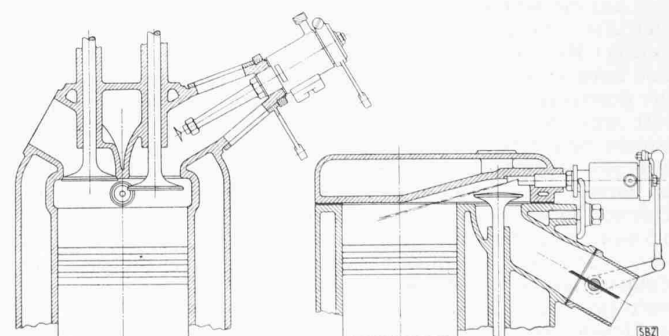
Die Anordnung der elektromagnetischen Einspritzdüse von Caproni a) Einbau bei obengesteuertem Motor. b) Einbau bei Seitenventilen
